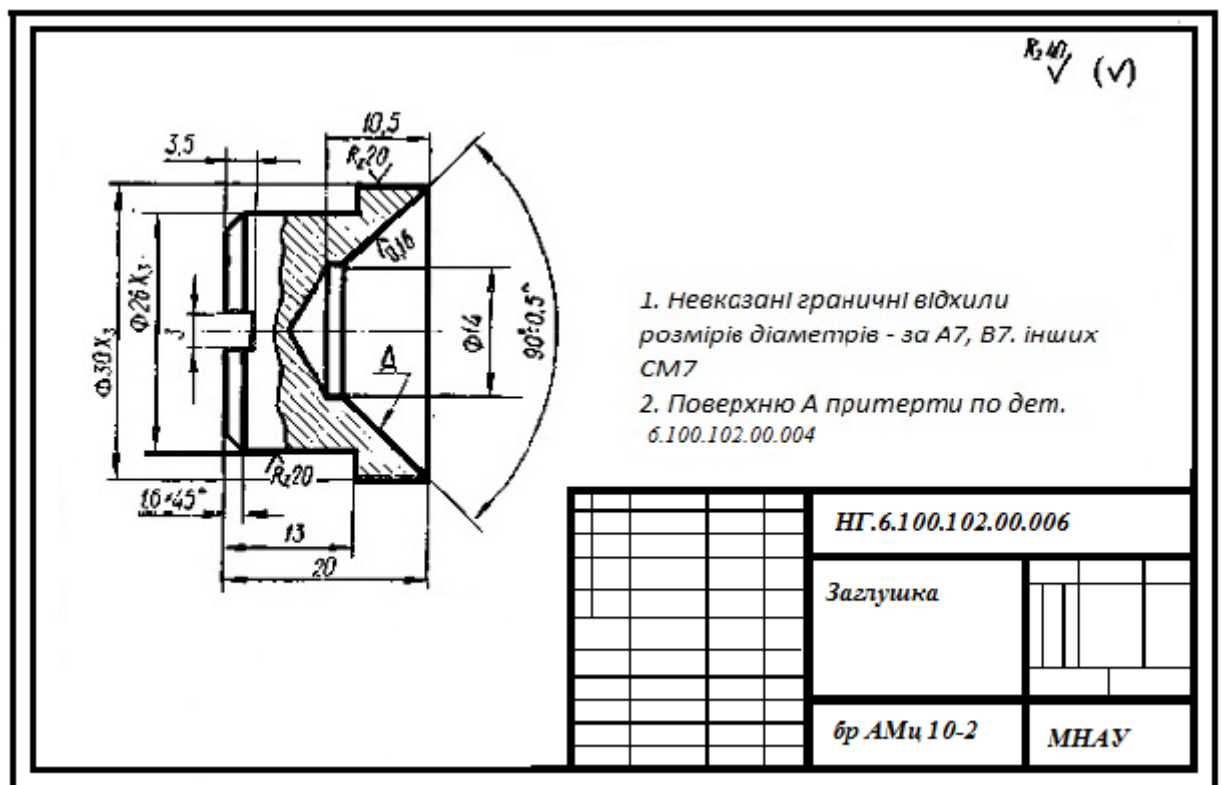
Робоче креслення деталі подвійного зворотного клапана
